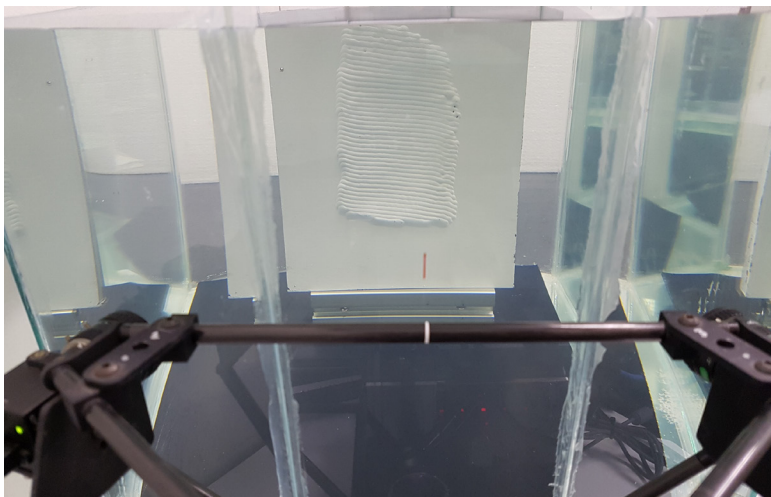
Vista frontal da cavidade preenchida com cordões de solda posicionada no interior do tanque para a medição.
